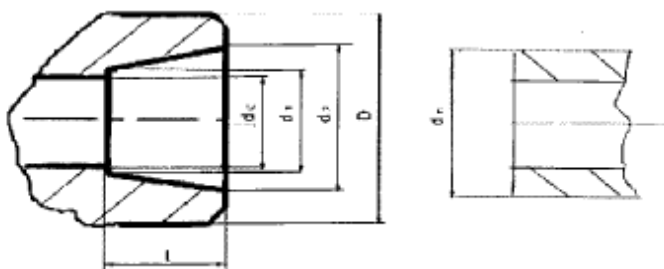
Общая часть соединительной детали для сварки нагретым инструментом вращающимся
